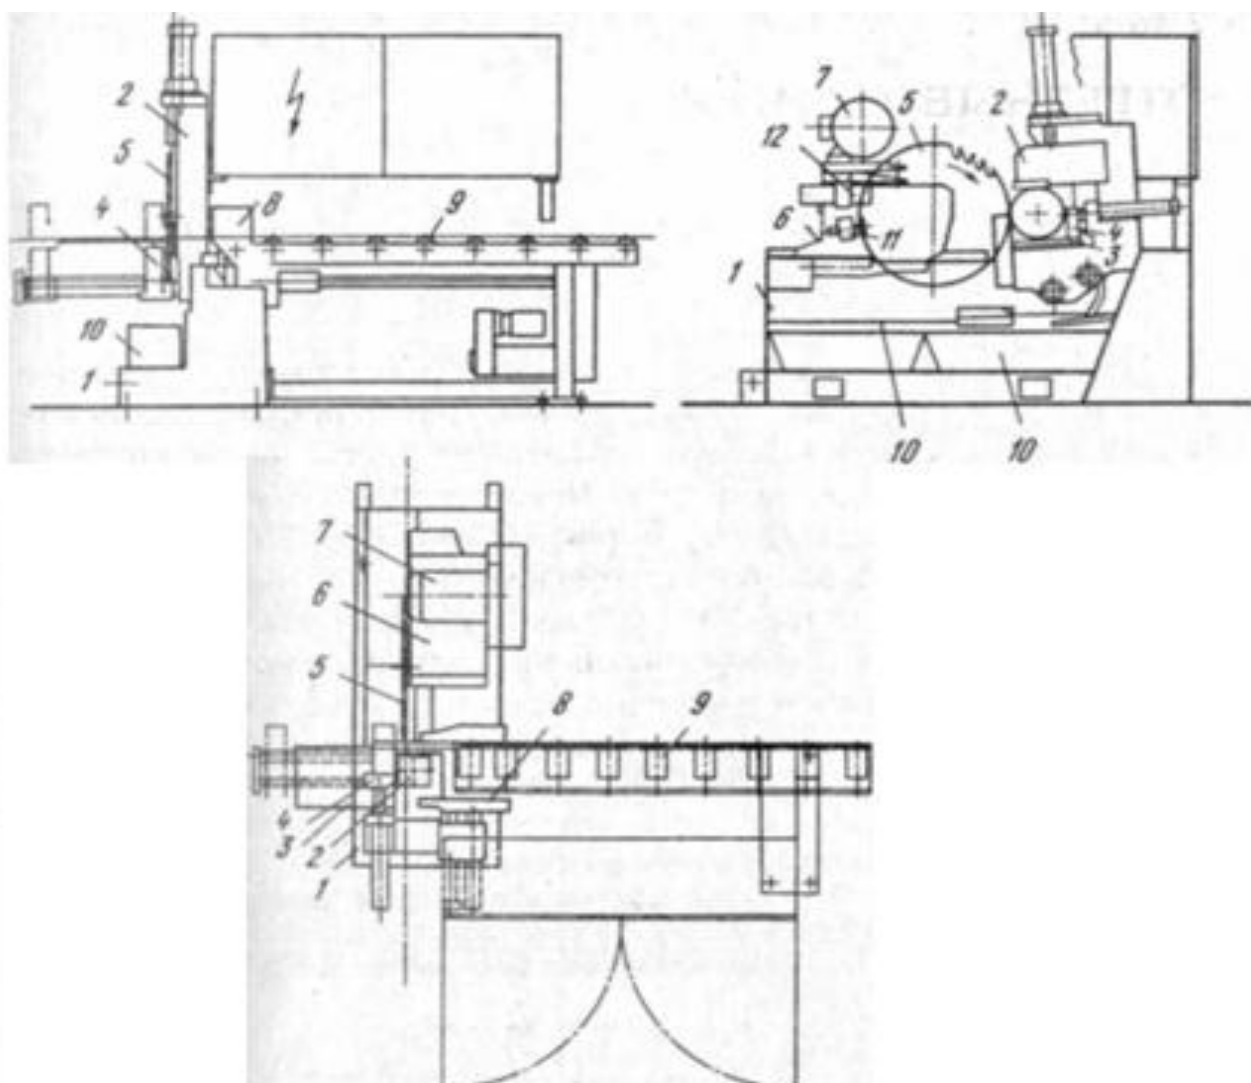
Общий вид станка, работающего дисковой пилой: 1 - станина, 2-4 - устройства для зажима заготовок в вертикальной и горизонтальной плоскостях; 3 - плита для размещения отрезанного материала; 5 - пила; 6 - салазки, осуществляющие движение подачи; 7 - главный привод; 8 - рейфер
